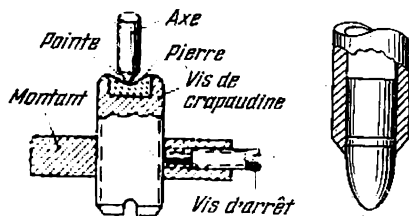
Montage de l'équipage mobile sur des axes; crapaudine et pointe sertie dans le tube de l'axe
